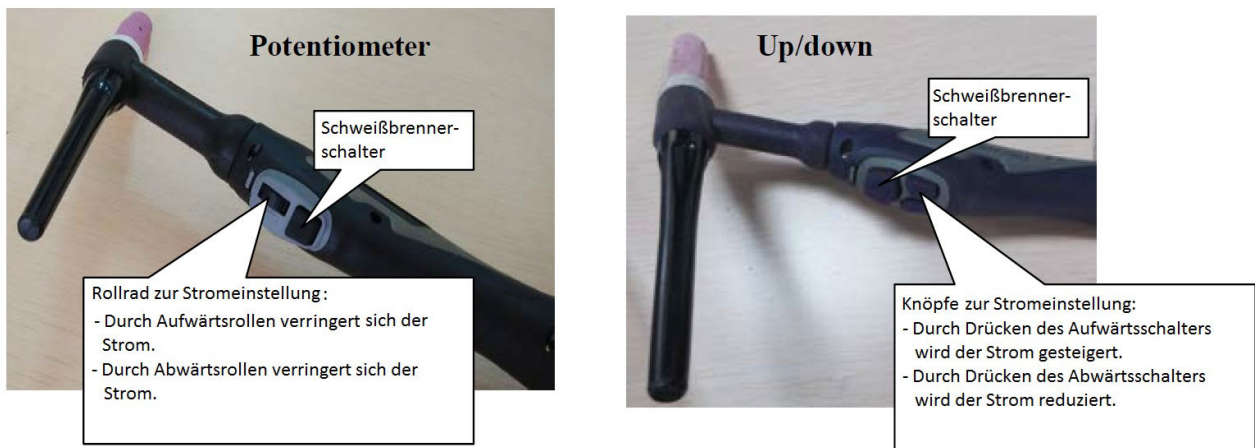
Schweißpistole-Brennerwechsel
